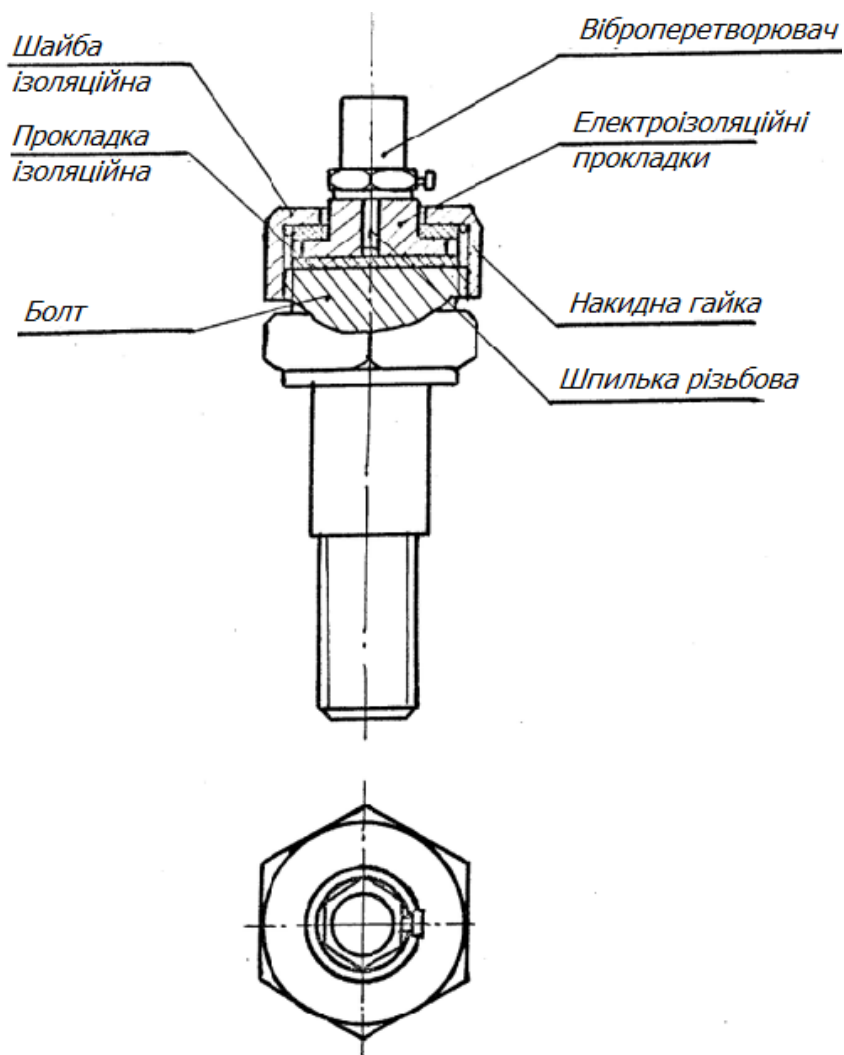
Креслення схеми кріплення віброперетворювача
